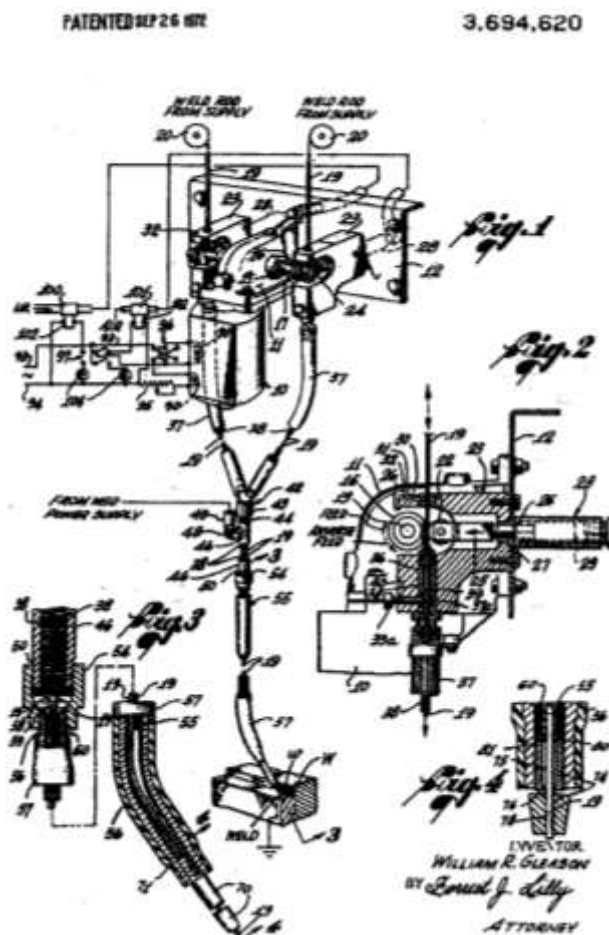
Устройство для наплавки с двойной подачей сварочной проволоки, разработанное Вильямом Р. Глисоном
